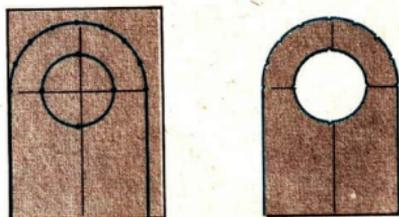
/3 Angerissenes und angekörntes Werkstück; fertig bearbeitetes Werkstück
